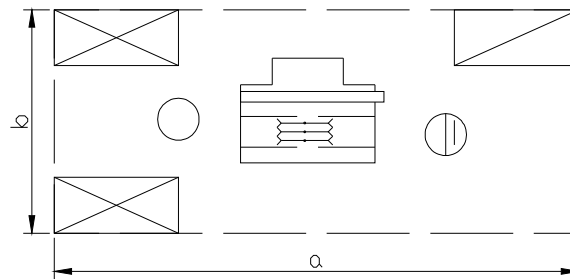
Схема организации рабочего места у многопильного круглопильного станка для продольного раскря пиломатериалов:
